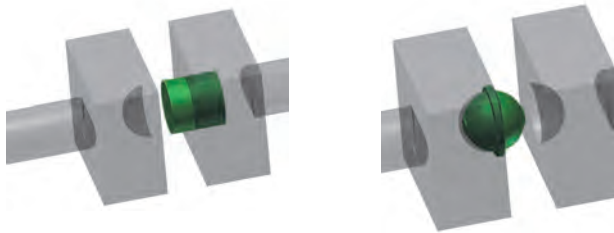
Pressen der Rohkugel aus einem Drahtstück
